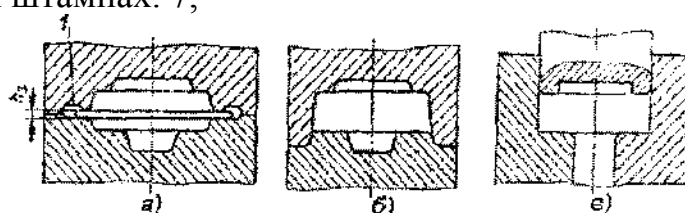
Схемы штамповки в открытых и закрытых штампах: 1 - облойная канавка
